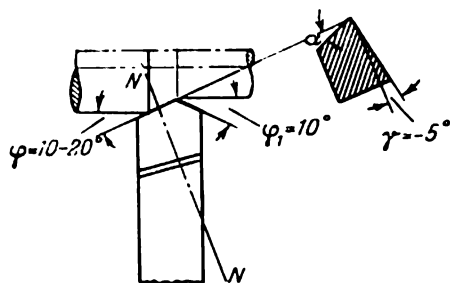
Outil KBEK pour tournage rapide des aciers difficilement usinables
